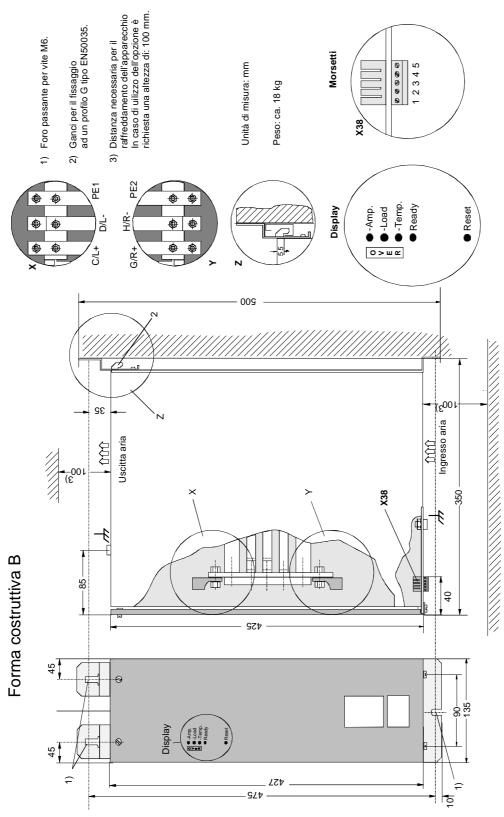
Dimensioni di ingombro per forma costruttiva B
